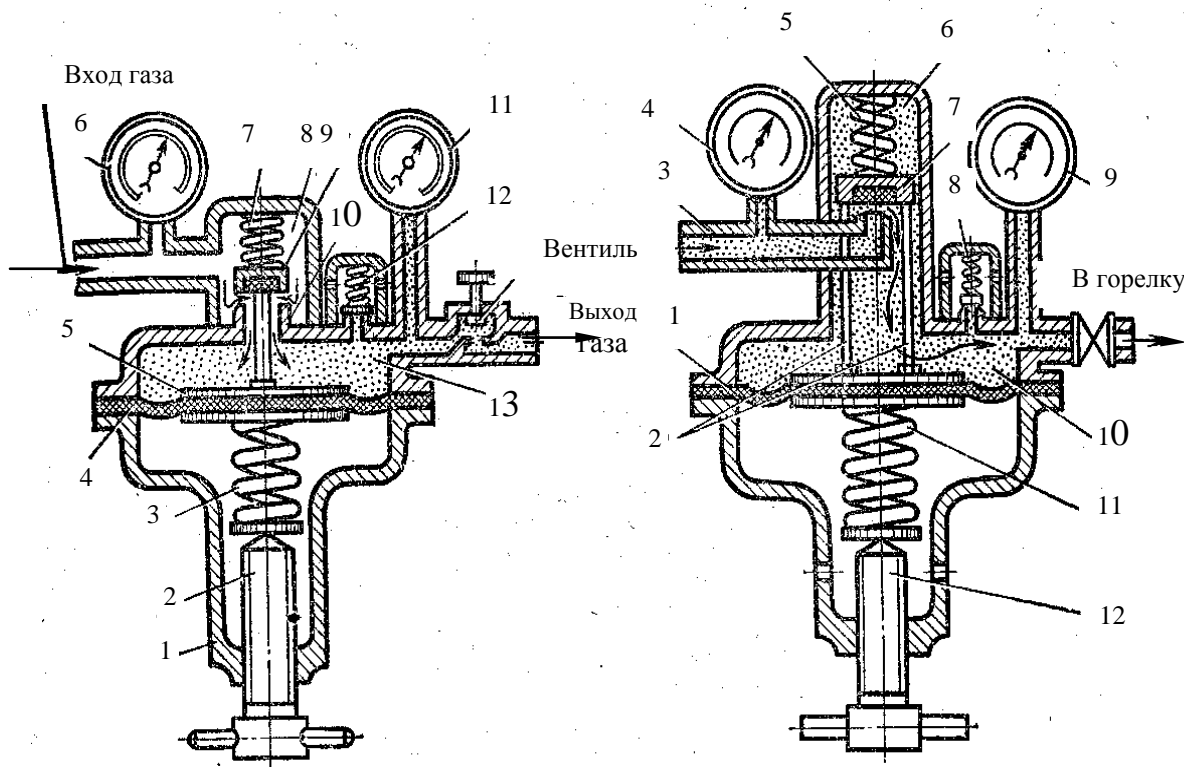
Схема кислородного редуктора: 1 – крышка, 2 – регулирующий винт; 3 – нажимная пружина; 4 – резиновая мембрана; 5 – шток; 6 – манометр; 7 – обратная пружина; 8 – камера высокого давления; 9 – клапан; 10 – седло клапана; 11 – манометр; 12 – предохранительный клапан; 13 – камера низкого давления
